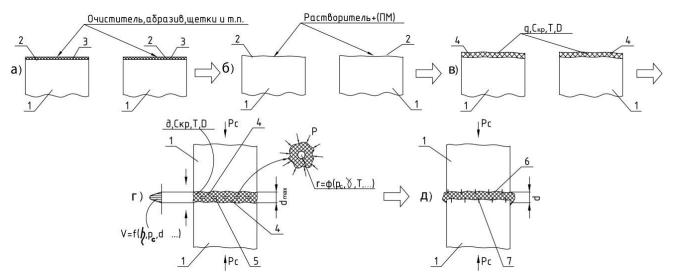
Физическая модель сварки ПМ жидким при комнатной температуре растворителем: 1 - соединяемые детали; 2 - свариваемые поверхности; 3 – загрязнения (смазка, жиры, пыль и т.п.); 4 – присадочный материал, содержащий растворитель; 5 - воздушное включение; 6 - сварной шов; 7 – межмолекулярные связи. t_i – текущее время; $t_{\rm ob}$ - продолжительность открытой выдержки; $t_{\rm cb}$ – продолжительность сварки; $p_{\rm c}$ - давление во время фазы образования соединения; $p_{\rm rn}$ -давление газового пузырька; $p_{\rm rn}$ = $p_{\rm c}$ + $2\gamma/r$, γ - поверхностное натяжение присадочного материала; T - температура деталей; V - скорость течения расплава; η – вязкость расплава; $R_{\rm z}$ - параметр шероховатости свариваемых поверхностей; g – расход присадочного материала; $C_{\rm kp}$ – критическая концентрация растворителя, соответствующая переходу смеси полимер+растворитель из расплавленного (жидкого) в твердое состояние; D – коэффициент диффузии растворителя в ПМ; $d_{\rm max}$ – максимальная толщина размягченного слоя, $d_{\rm max}$ = $\beta g/C_{\rm kp}$; $t_{\rm cb}$ = g^2/α $C_{\rm kp}$ 2 D; α , β – постоянные. a, δ , e – t_i = 0; e - t_i = $t_{\rm ob}$; θ - t_i = $t_{\rm ob}$ + $t_{\rm cb}$.
